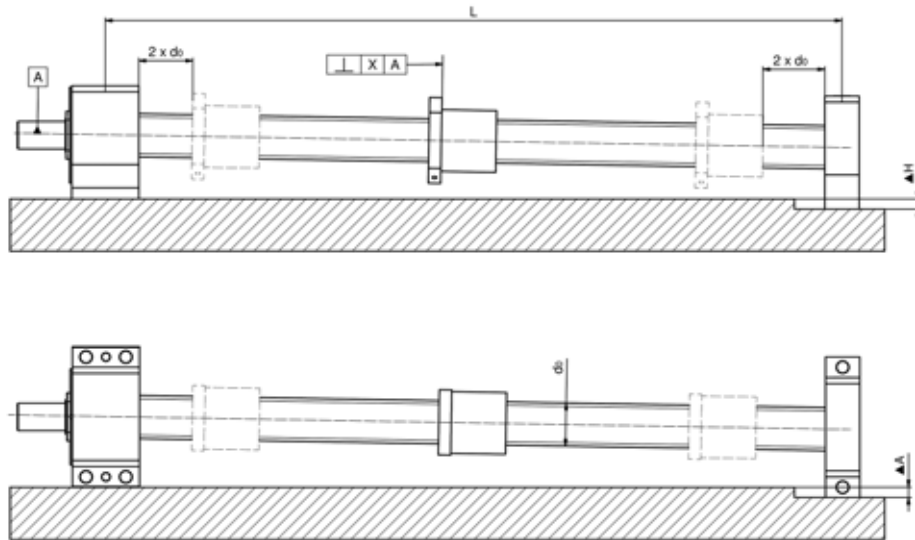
Definition der Montagetoleranzen von Kugelgewindetrieiben
